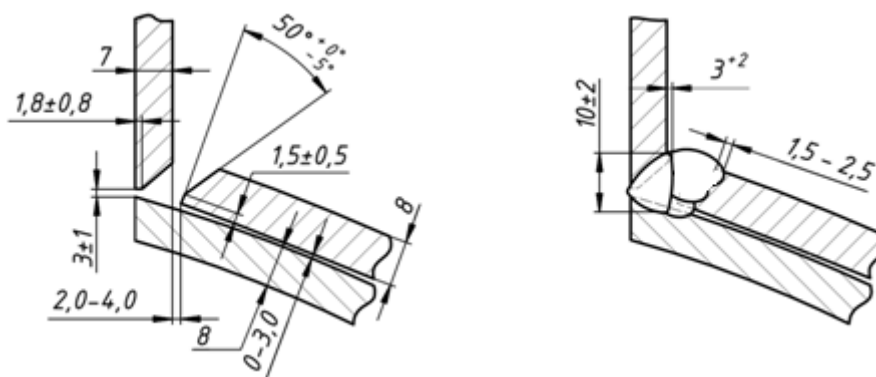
Нестандартный сварной шов №2
